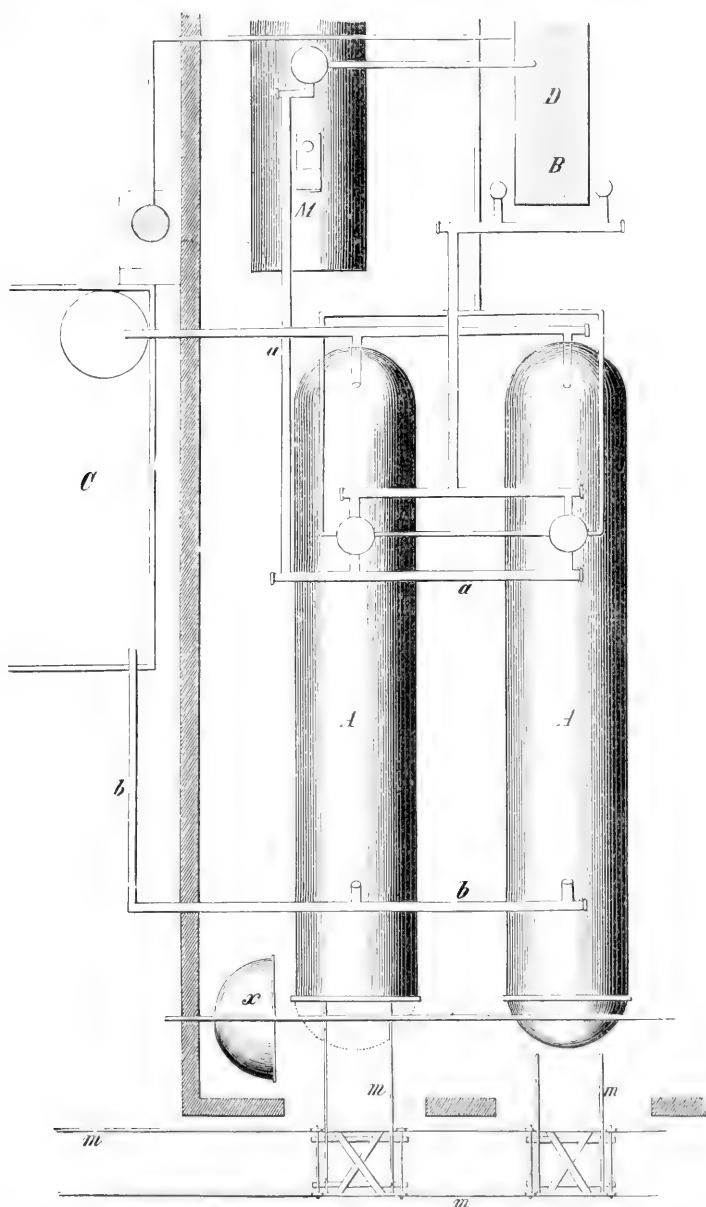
Einrichtung einer Anstalt behufs Imprägnierung nach dem Dampfdruckverfahren.
